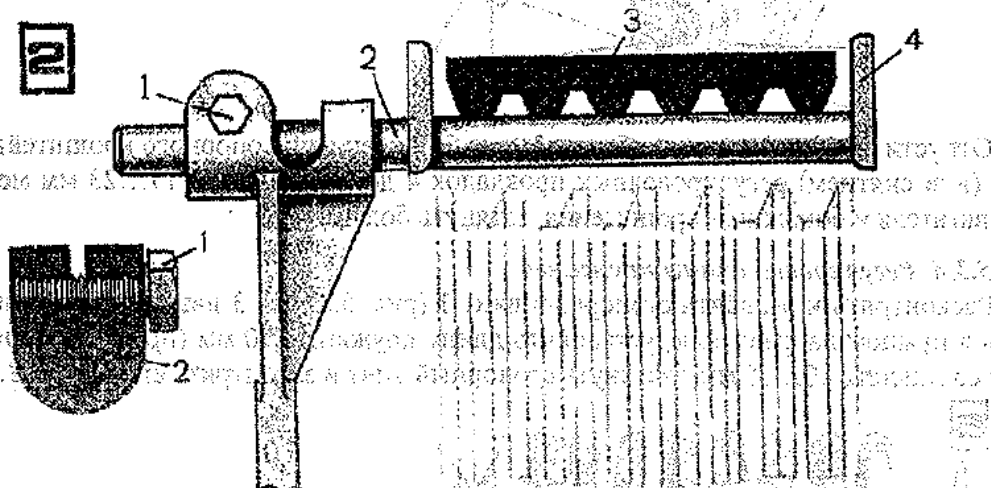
Схема регулировки положения пальца подъемника: 1 - болт стяжной; 2 - палец; 3 - ремень; 4 - направляющие щечки
